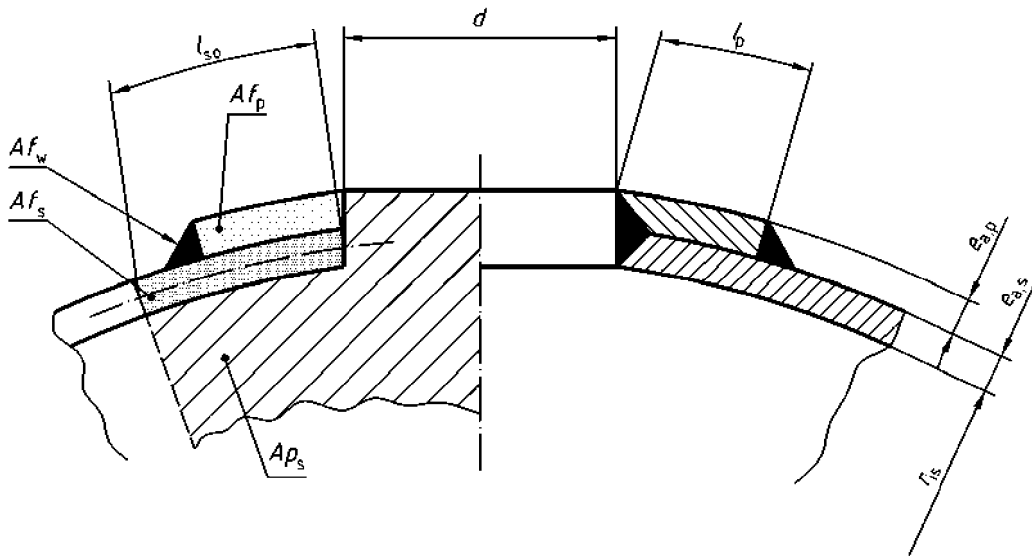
Envoltente esférica o fondo o cóncavo con abertura aislada y placa de refuerzo
